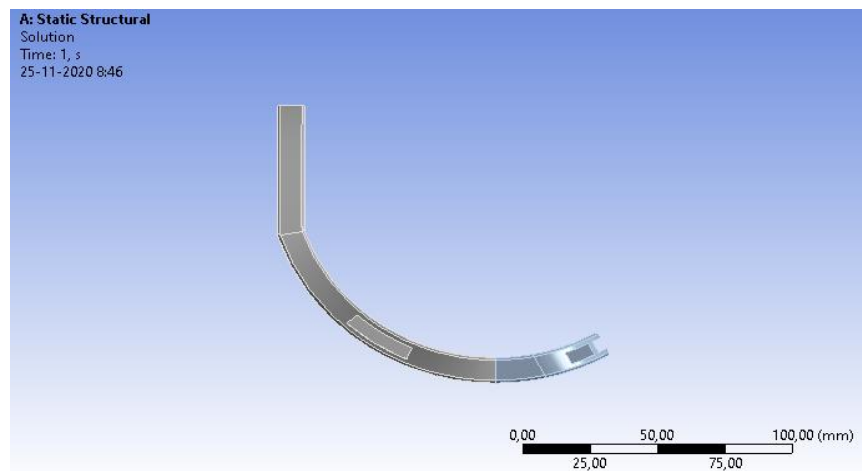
Vista 5 rediseño N°1 de eslabón pierna izquierda.
